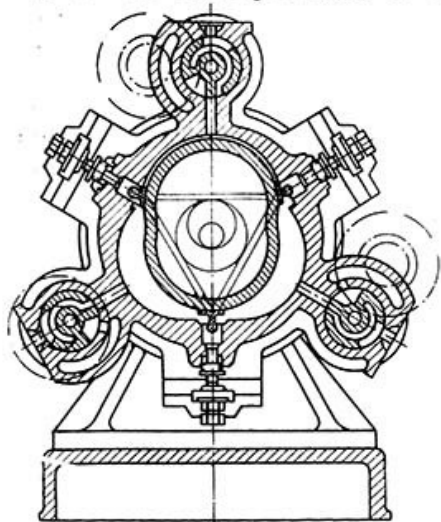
Схема роторно-поршневого двигателя Грея и Драммонда (1909 г.)
